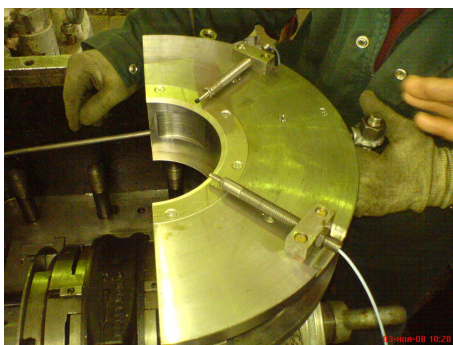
Смонтированные датчики на «трубках-удлинителях» КНД и КВД компрессора поз.105J
